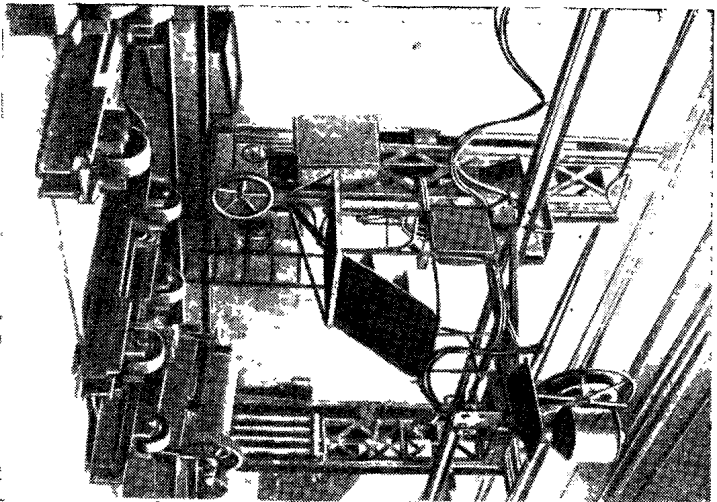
Установка с подъемными путями для сварочного трактора.
